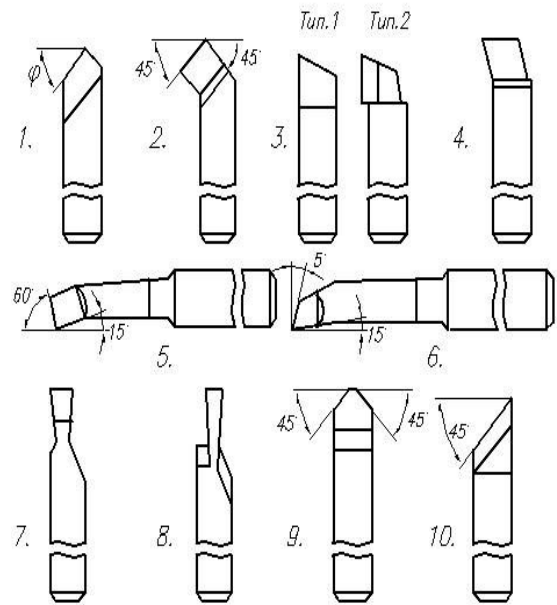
Резцы токарные с пластинкой из быстрорежущей стали.
